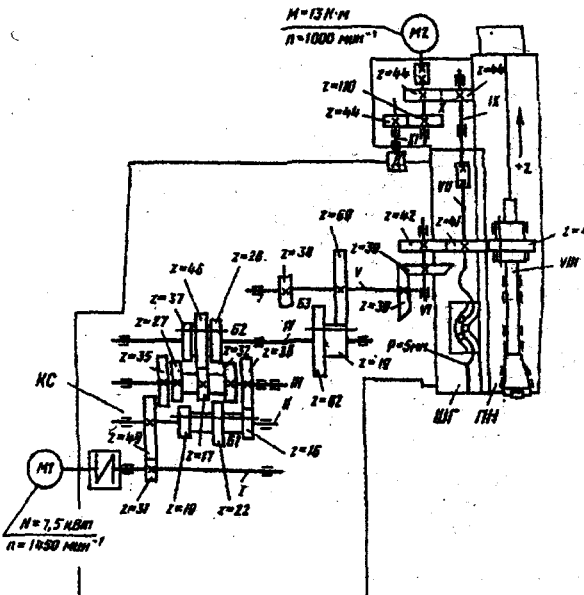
Кінематична схема головного привода фрезерного врістата мод. 6Р13Ф3
